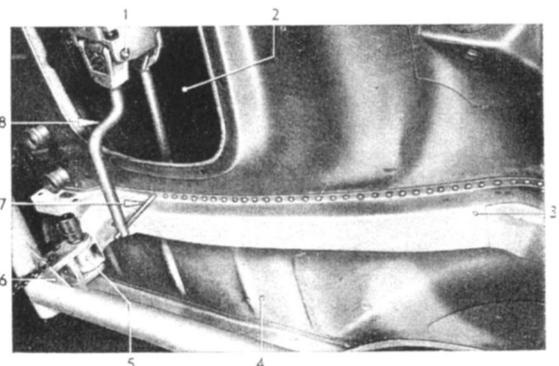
Längsträgerhinterteil an Bodenblech punktschweißen – Bild zeigt Punktschweißzange durch Öffnung für Kraftstoffbehälter eingeführt
